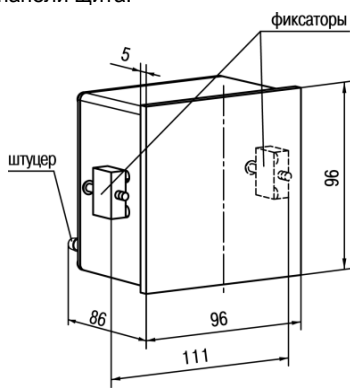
Габаритные размеры преобразователя щитового крепления
